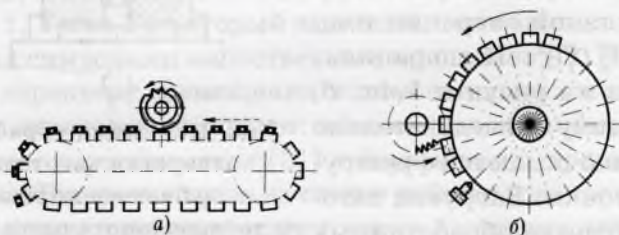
Схемы операций обработки заготовок на фрезерных полуавтоматах:
